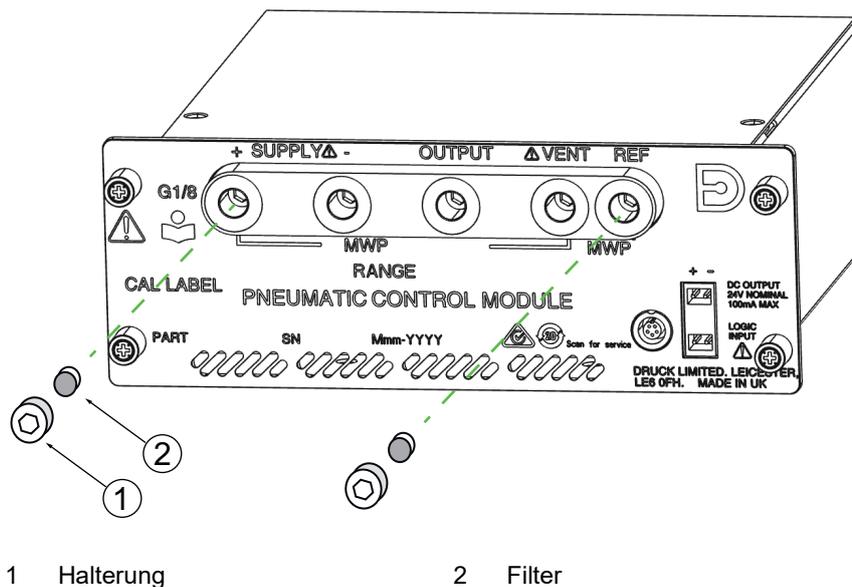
Austausch des Filters des pneumatischen Steuergeräts
